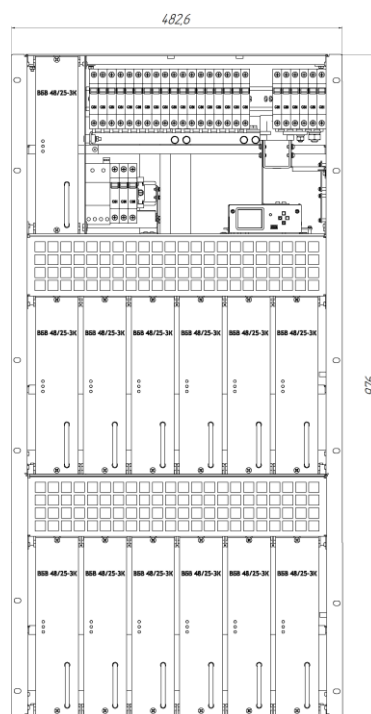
Габаритный чертеж УЭПС-3К 48/100-44 (ВЭ), УЭПС-3К 60/80-44
